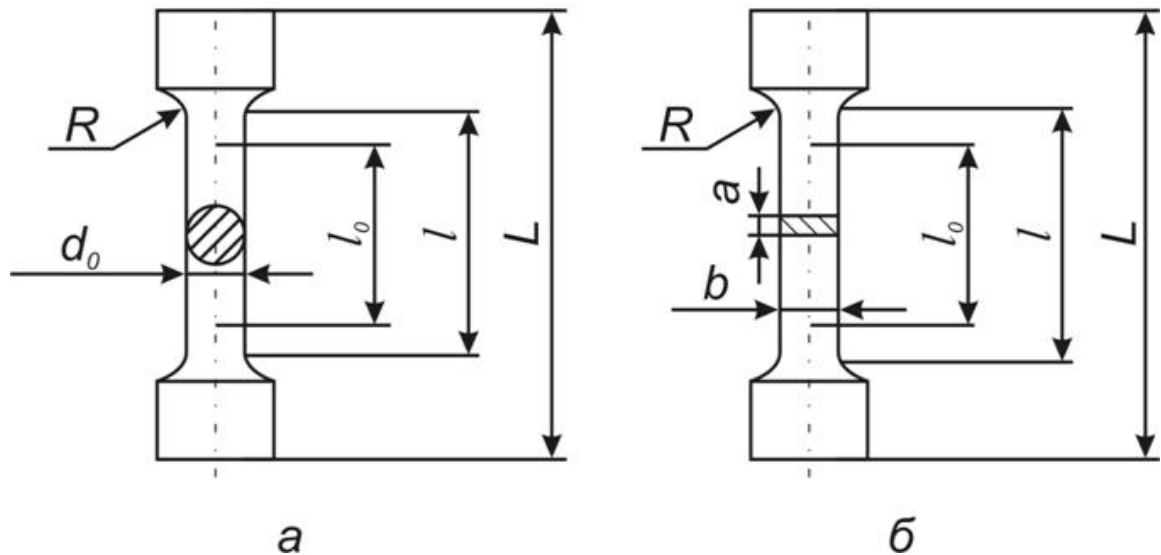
Образцы для испытаний: *a* – круглый образец; *б* – плоский образец; L – общая длина; l – рабочая длина; l_0 – начальная расчетная длина; d_0 – диаметр образца до испытания; a – толщина; b – ширина; R – радиус скругления.
